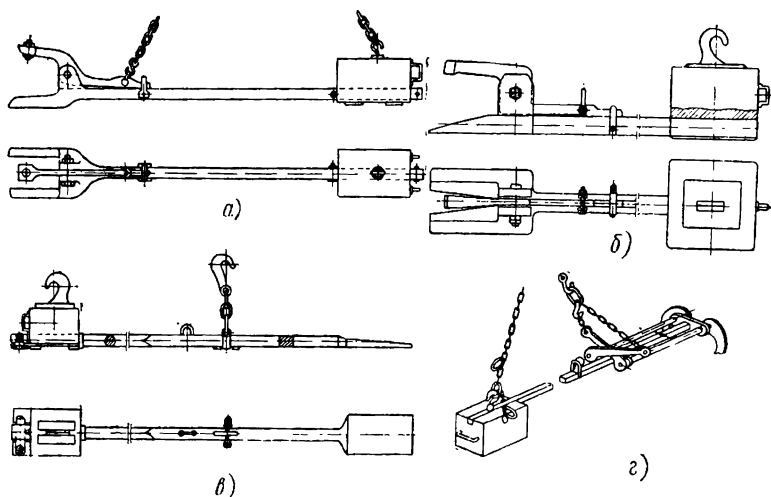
Приспособления для посадки в печь заготовок и слитков небольшого веса и выдачи их из печи: а и б — вилки с противовесами и зажимными рычагами; в — лопата с противовесом; г — клещи с противовесами
